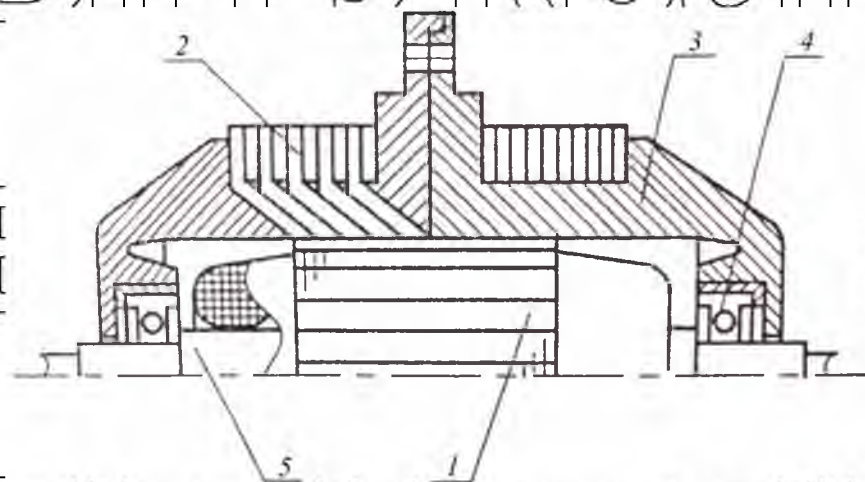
АД із зовнішнім двопаке́тним ротором: 1 – статор; 2 – ротор; 3 – корпус; 4 – підшипник; 5 – нерухома вісь
